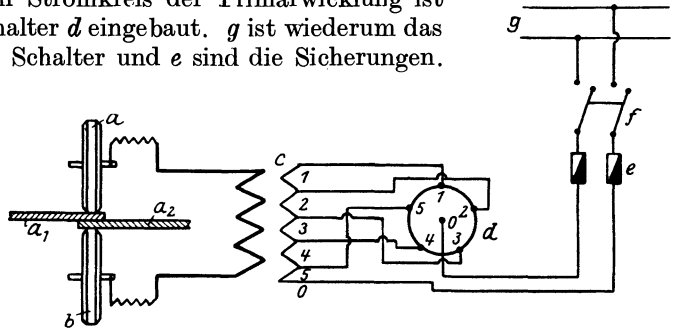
Schaltung und Stromzuführung bei Nahtschweißmaschinen.
